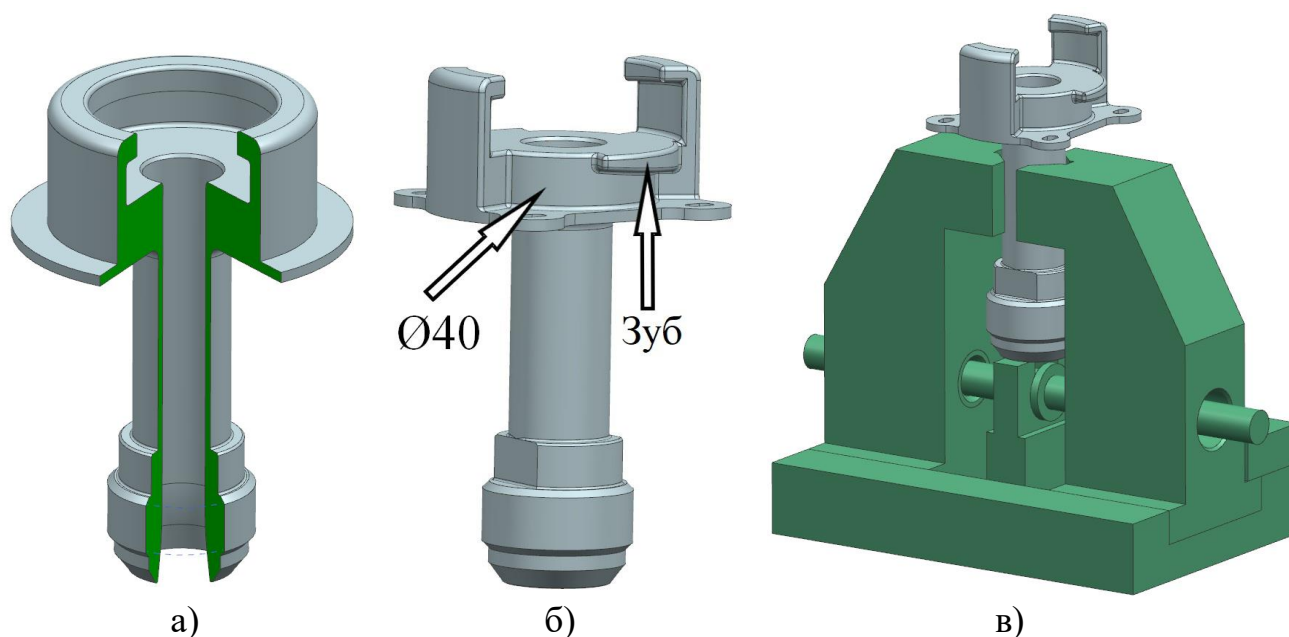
Деталь «Фланец»: а) 3D -модель заготовки, б) 3D -модель детали, в) 3D – модель приспособления – схема установки и закрепления
